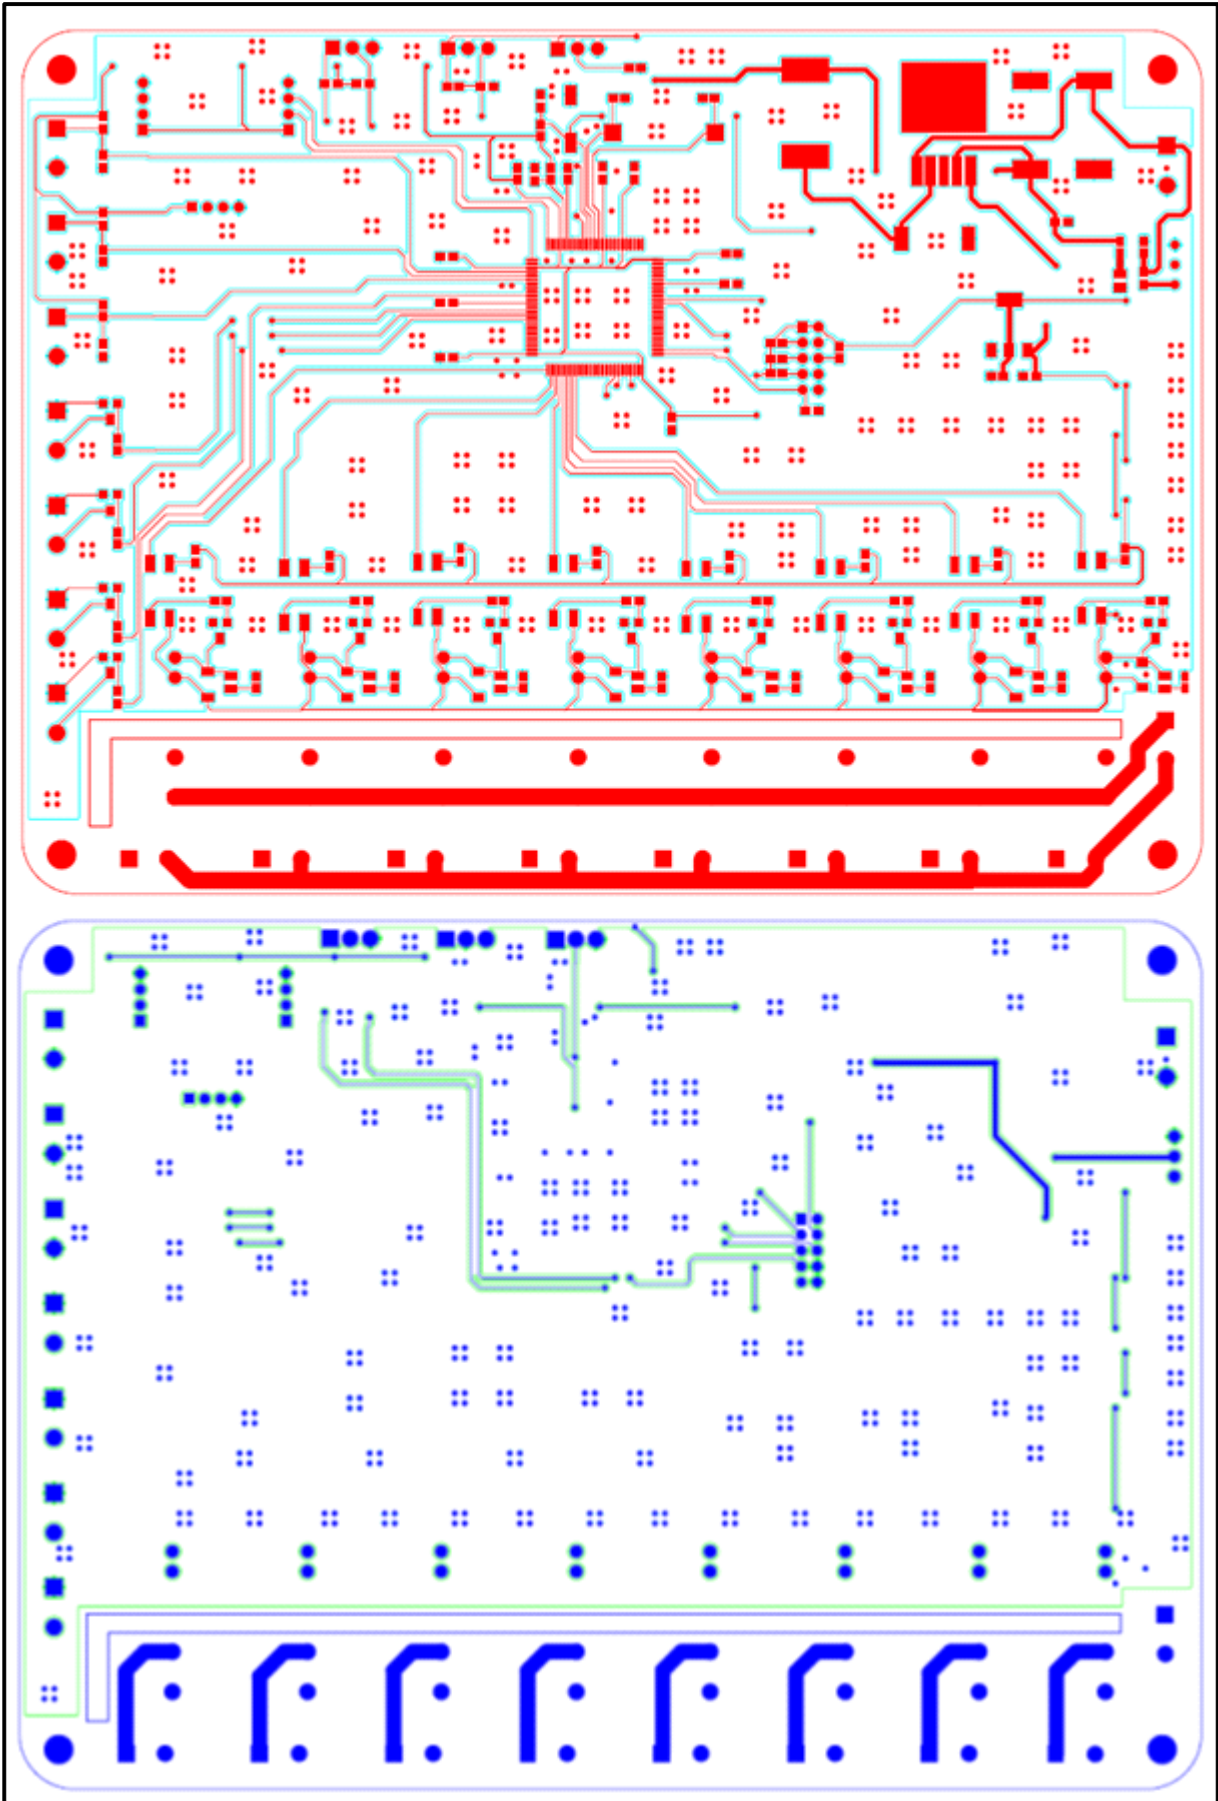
PCB 기판 설계도 Top 및 Bottom
